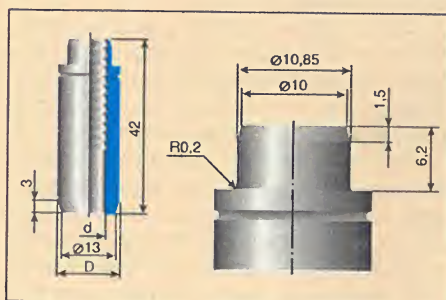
Направляющие втулки впускных клапанов двигателей ВАЗ-2101...-2106.
